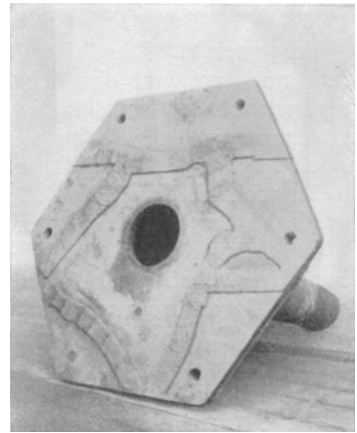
Ständerplatte nach der Schweißung.
